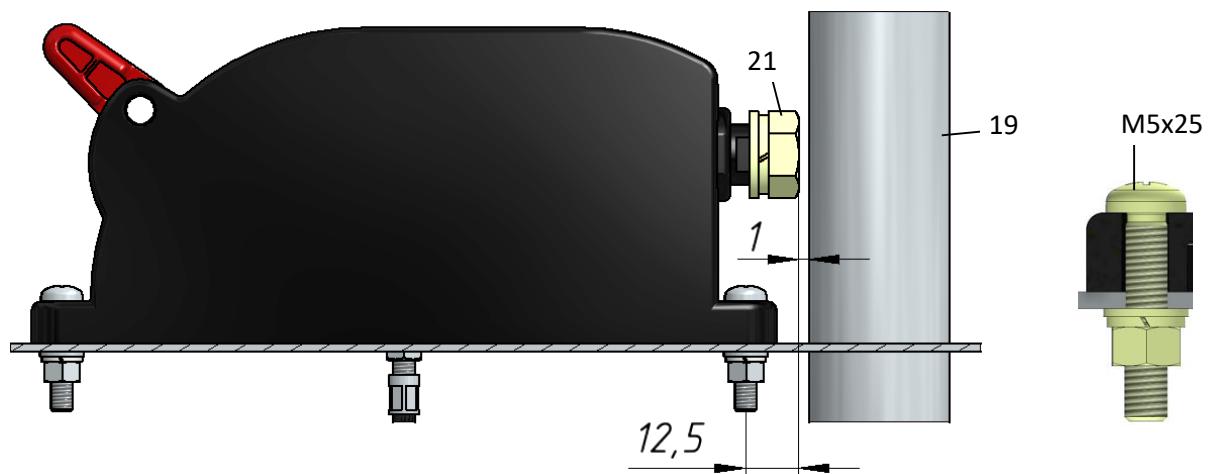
Установка блокиратора на ВЭ с червячным редуктором
